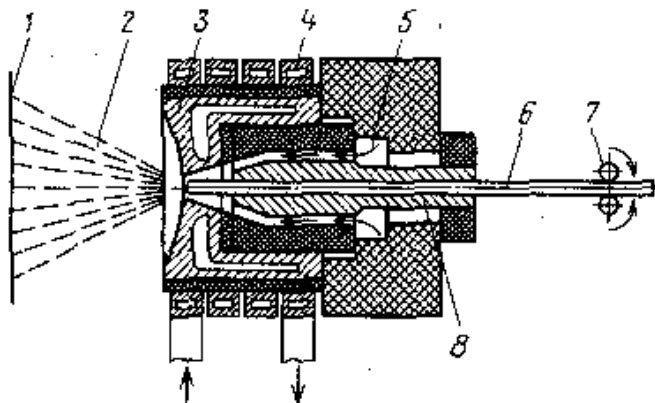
Роспилювальна головка високочастотного напилювання: 1 – поверхня для напилювання; 2 – газометалічний струмінь; 3 – концентратор струму; 4 – індуктор; 5 – повітряний канал; 6 – дріт; 7 – подаючі ролики; 8 – спрямовувальна втулка
